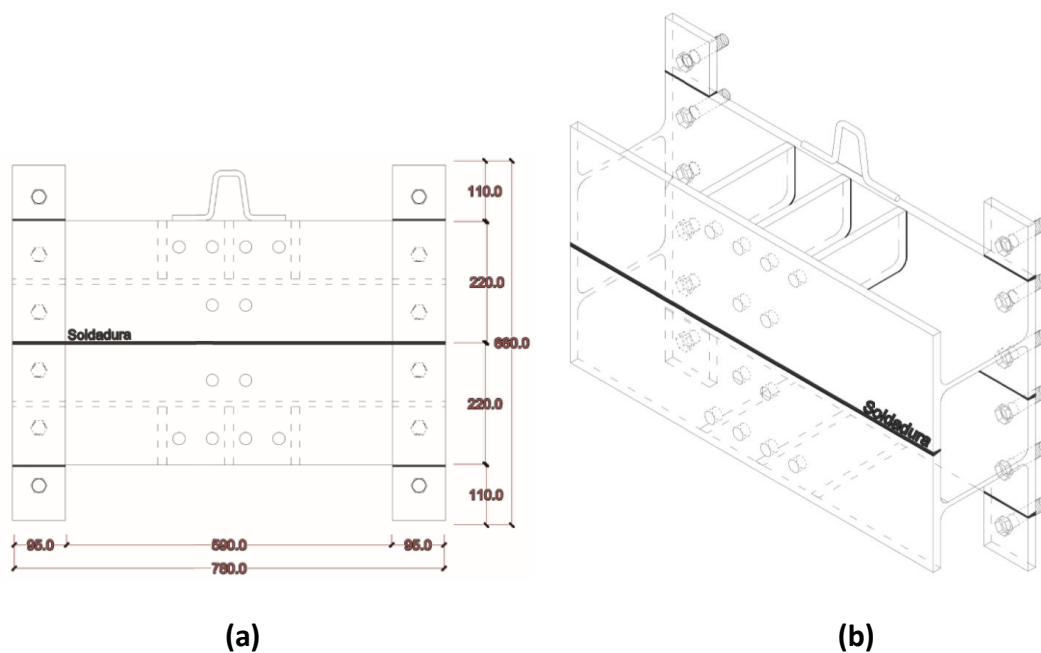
Suporte para fixação do pórtico. (a) Vista frontal. (b) Perspectiva isométrica.
